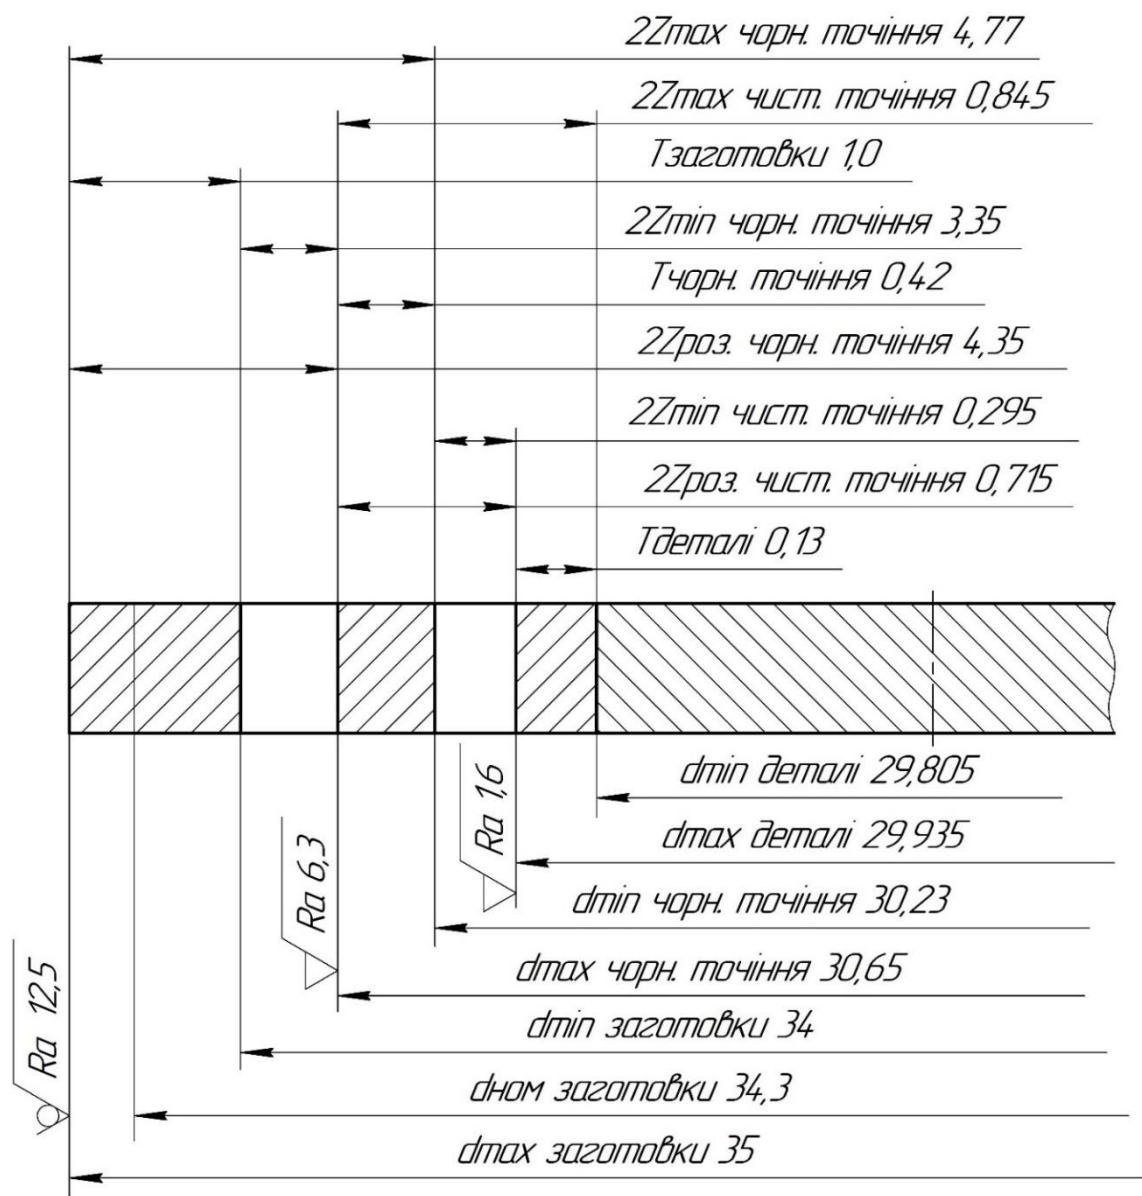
Схема припусків і допусків для обробки діаметра 30d11
